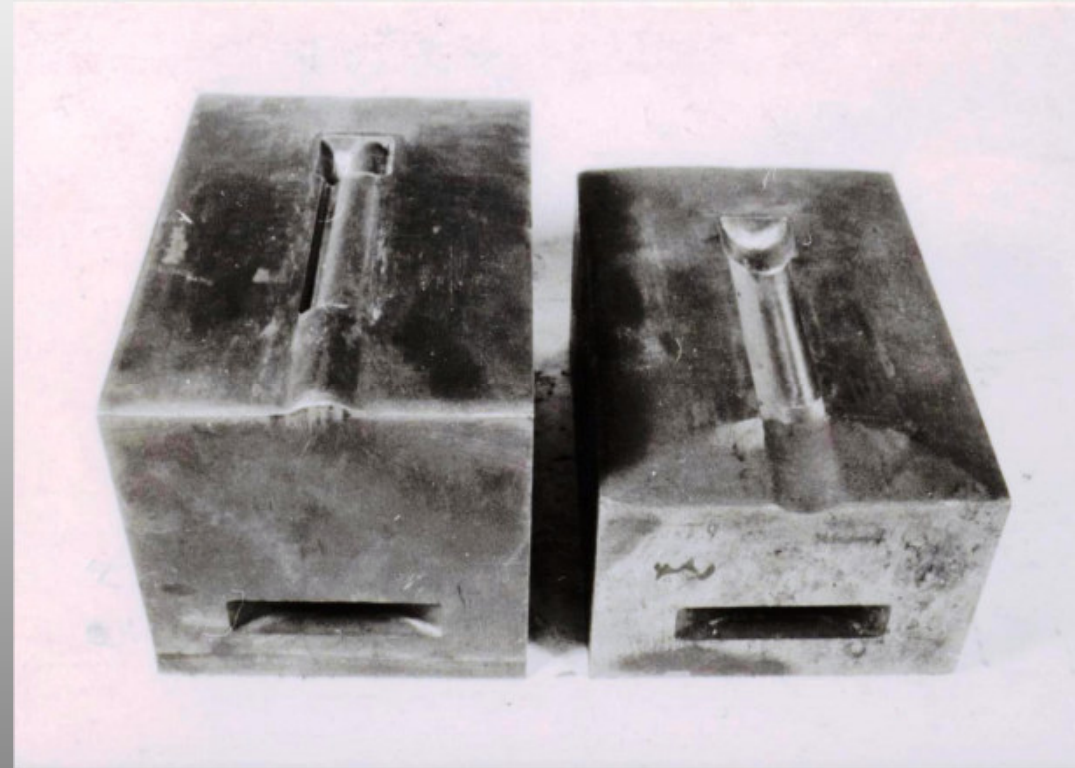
Pressengesenk mit Führungen im Gesenkhalter und Schraubenbefestigung
